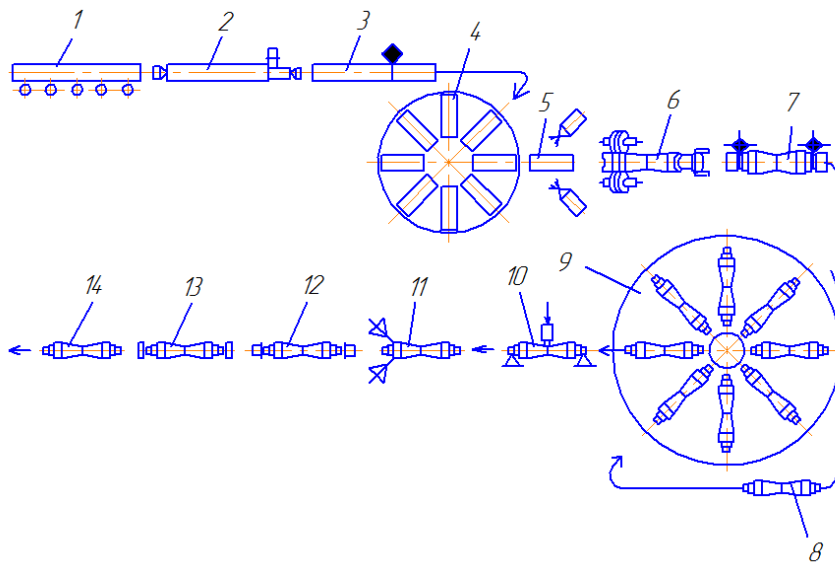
Схема маршрутного технологічного процесу виготовлення чорнових осей: 1 – надходження заготовок зі складу; 2 – зачищення штанг; 3 – поділ штанги на заготовки; 4 – нагрів заготовок; 5 – гідрозбивач окалини; 6 – прокатка осі; 7 – відрізання технологічних кінців; 8 – таврування; 9 – нормалізація; 10 – виправлення; 11 – очищення окалини; 12 – фрезерування торців; 13 – ультразвуковий контроль; 14 – подача на склад готової продукції
